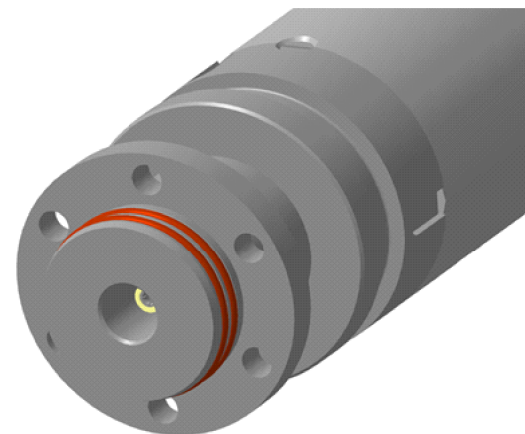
Внешний вид клапана КПУЭ-102 со стороны головки
